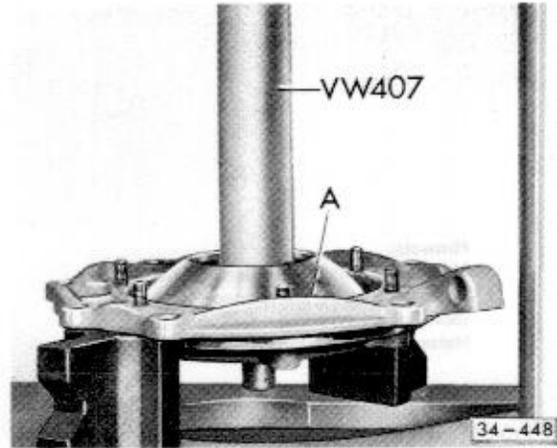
Rillenkugellager für Ausgleichgetriebe auspressen
